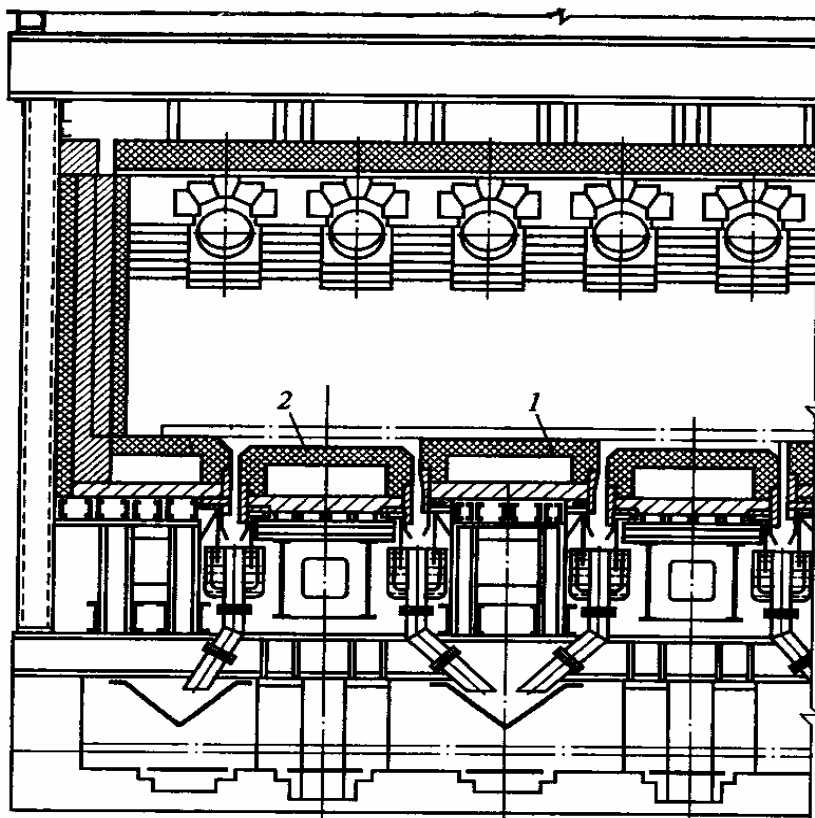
Поперечный разрез печи с шагающим подом: 1 – неподвижные балки; 2 – подвижные балки
